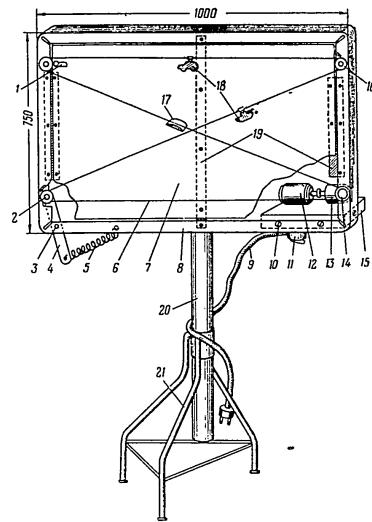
Прибор для тренировки в стрельбе по движущимся целям: 1 — отсекатели целей; 2 — ось с роликом; 3 — ось; 4 — стойка; 5 — оттяжная пружина; 6 — привод; 7 — экран; 8 — рамка; 9 — планка крепления экрана; 10 — шуруп; 11 — ролик; 12 — электродвигатель; 13 — редуктор; 14 — ведущий ролик; 15 — подставка; 16 — обработанный ролик; 17 — бруск; 18 — цели; 19 — планки крепления экрана; 20 — труба; 21 — тренога.
